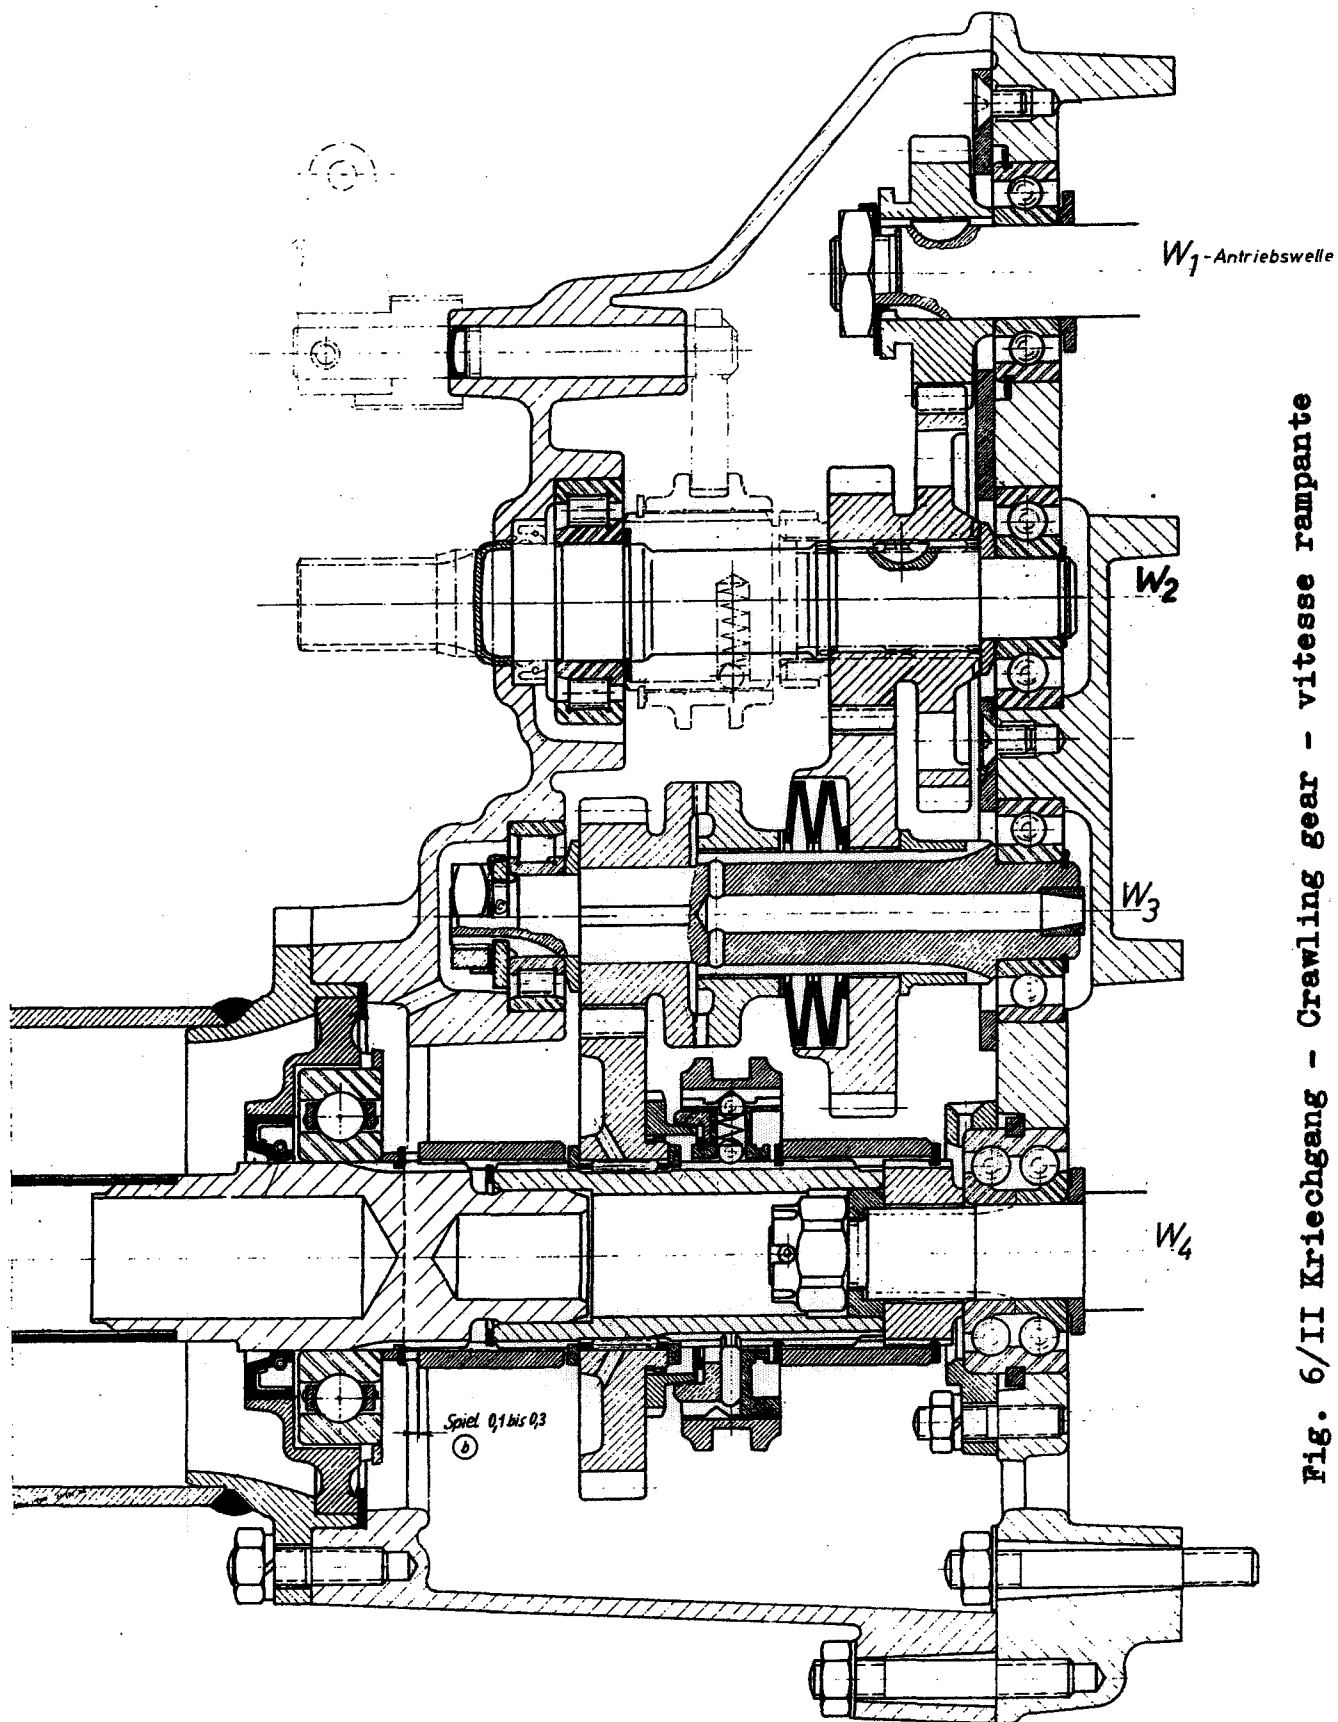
/II Kriechgang - Crawling gear - vitesse rampante
